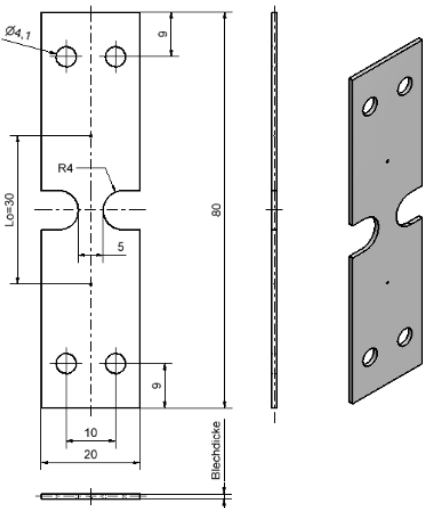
Geometrie der gekerbten Zugproben mit einem Kerbradius von 4mm
